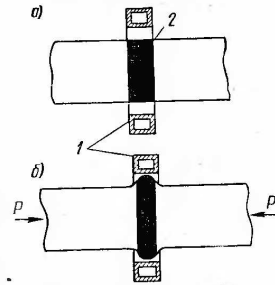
Схема сварки без оплавления: а — нагрев; б — осадка
